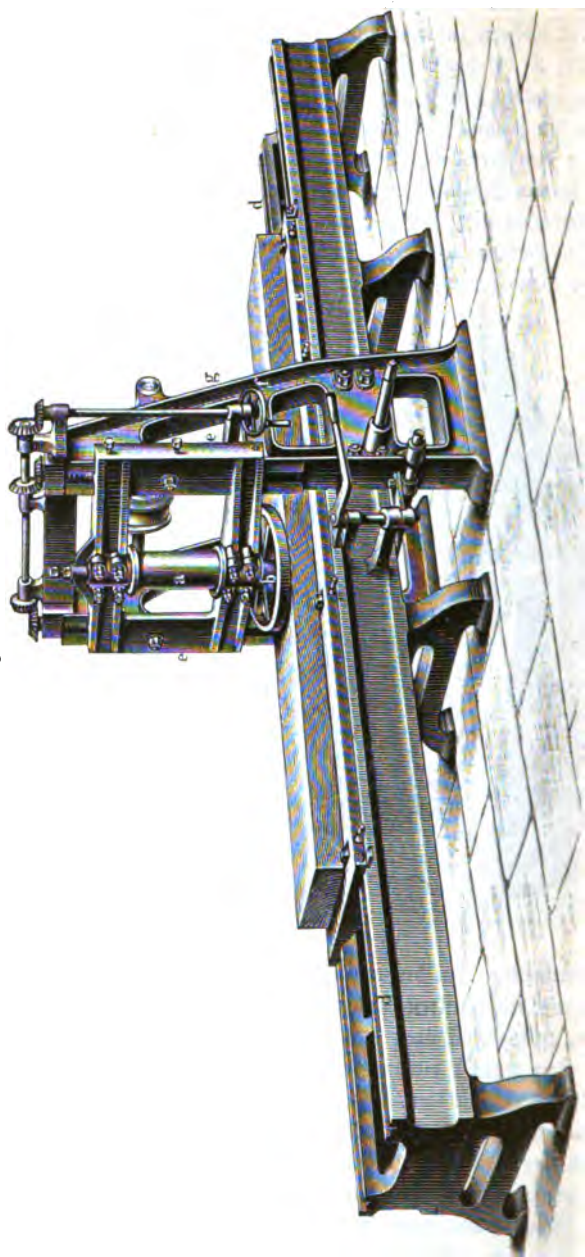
Die Messer ragen aus der unteren Fläche der auf der senkrechten Spindel *a* befestigten Scheibe *b* hervor, die durch einen auf *a* geführten halbgeschränkten Riemen schnell umgedreht wird, während das zu hobelnde Holz auf der Tischplatte *c* durch geeignete Spannvorrichtungen befestigt ist. Wenn diese in den prismatischen Führungen des Bettes *d* geleitete Tischplatte in der von den Metallhobelmaschinen her bekannten, in der Figur nicht näher erläuterten Art langsam verschoben wird, so wird durch die Messer oder stichelförmigen Schneiden der Scheibe *b* die obere Fläche des Holzes in der schon oben besprochenen Weise abgerichtet. Die Messerwelle findet hierbei ihre Lager in einem Rahmen *e*, der an den senkrechten Führungsbahnen des Gestelles *g* vermittels der beiderseits angebrachten Schraubenspindeln durch Umdrehung des Handrades *f* sehr genau verstellt werden kann, so daß man hierdurch nicht nur die Stärke des abzunehmenden Spanes in der Hand hat, sondern auch den jeweiligen Dicken verschiedener Hölzer entsprechend die Stellung der Messerscheibe bestimmen kann.
